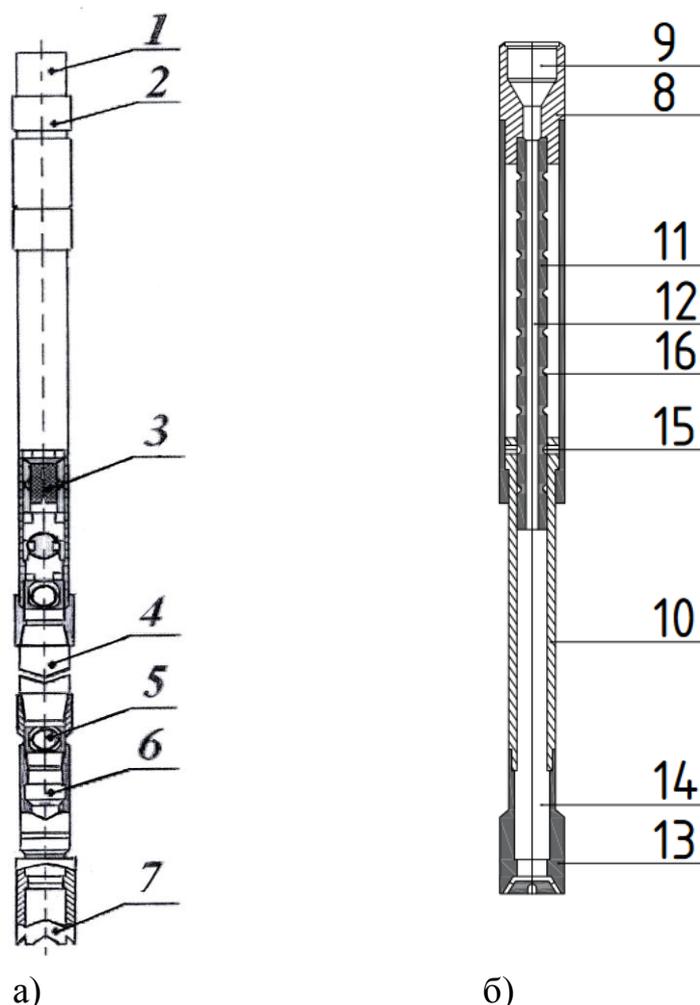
Комплекс оборудования для очистки скважины типа КОС-02
